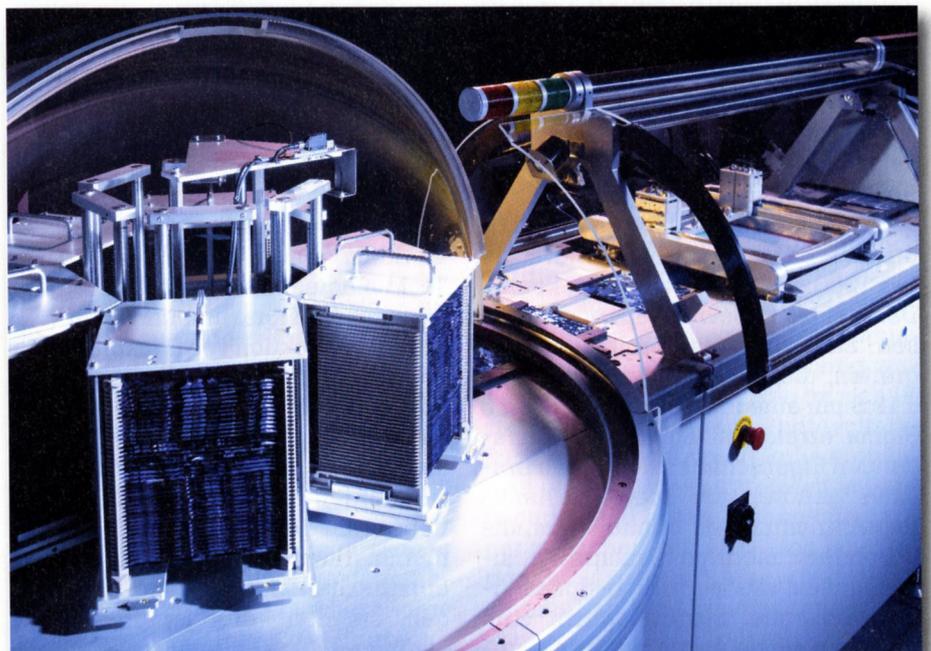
Ausschnitt mit Blick auf Printer und Stacker
